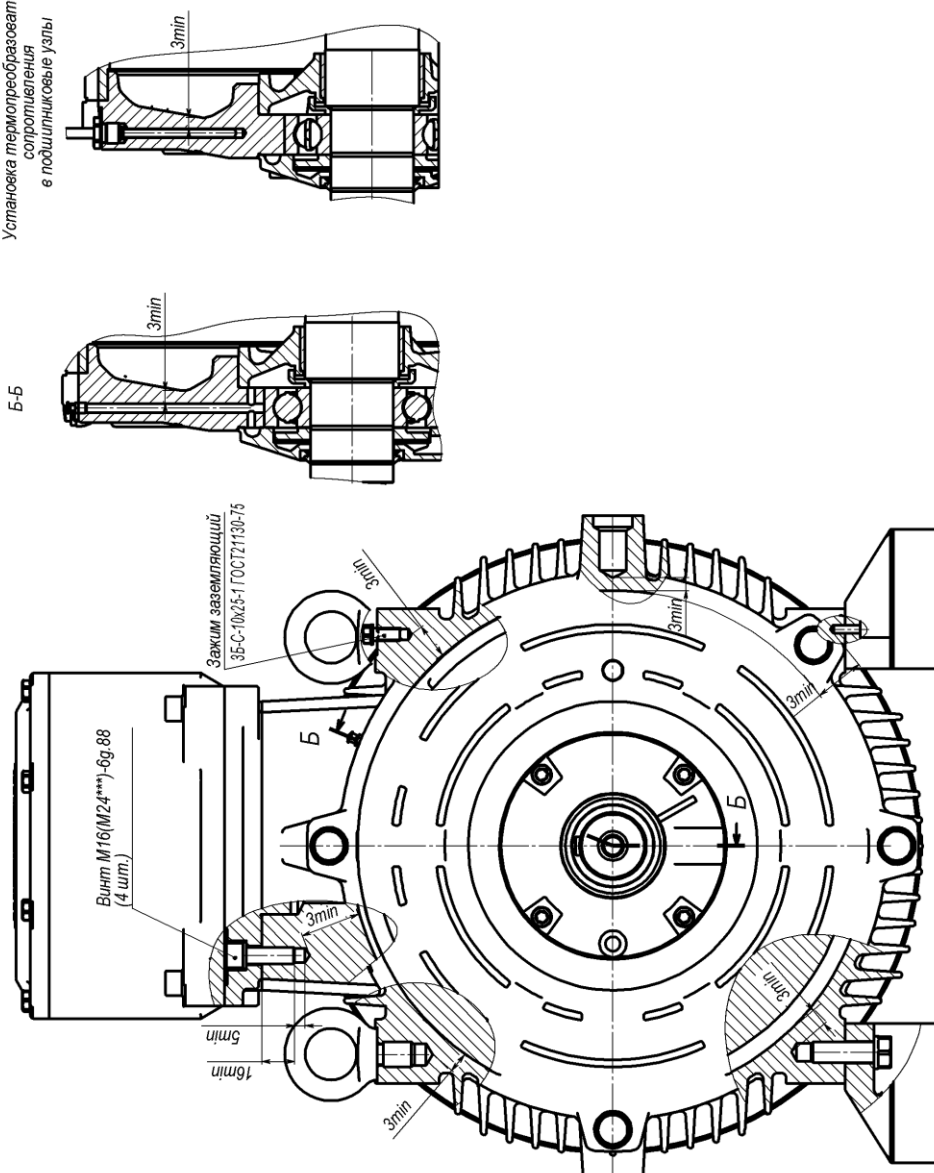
Чертеж взрывозащиты двигателей
